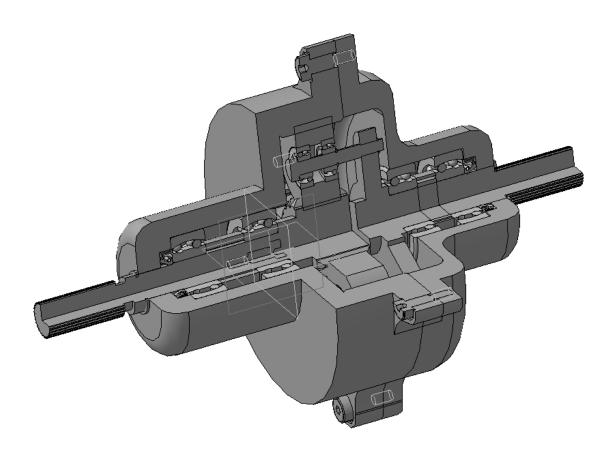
Пример зубчатого планетарного редуктора
